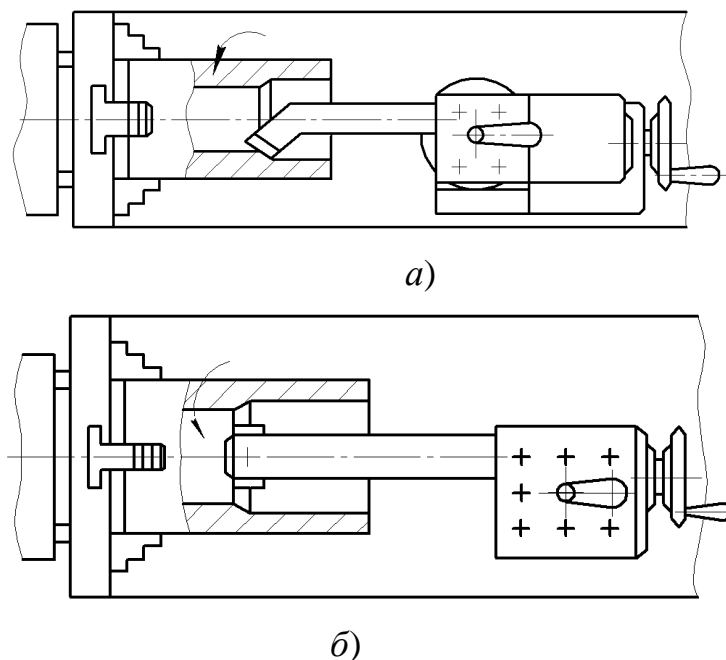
Схеми розточування на токарних верстатах:
